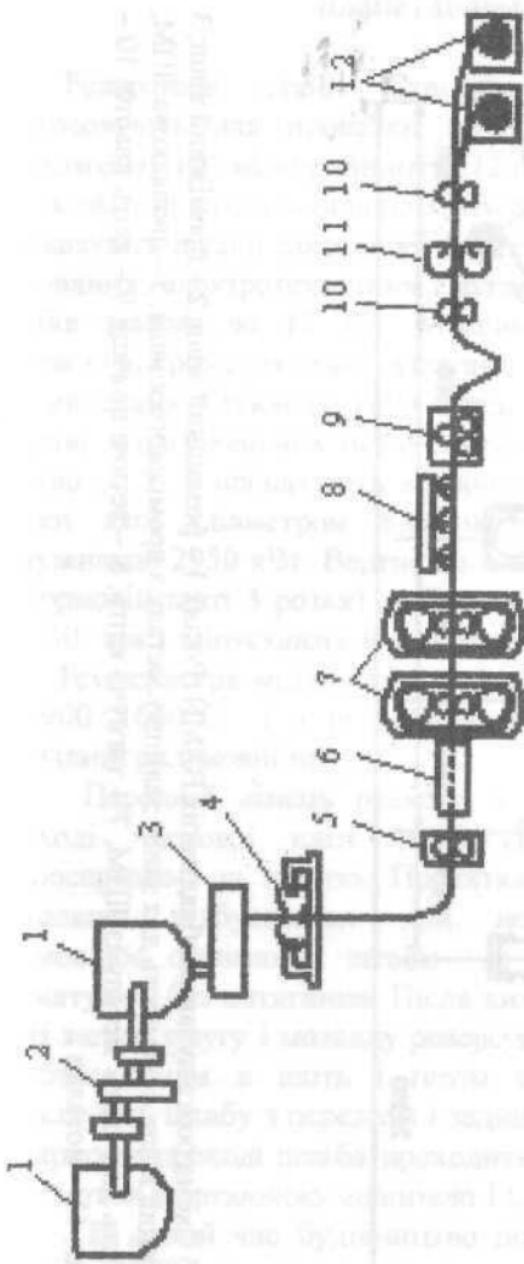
Схема розташування обладнання ВЛПМ в г. Крофордсвілі (США) [28]: 1 – розливний ковш; 2 – поворотний стенд; 3 – проміжний ковш; 4 – ливарно – прокатна машина; 5 – тягучий ролик; 6 – індукційний нагрівач; 7 – прокатні клеті; 8 – дільниця ламінарного охолодження, 9 – правильно – тягучий пристрій, 10 – тягучий пристрій, 11 – моталка; 12 – моталка
